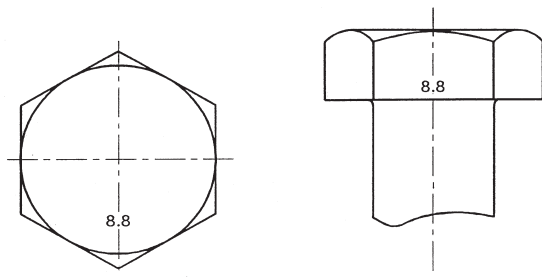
Abb. G: Beispiel für die Kennzeichnung von Sechskantschrauben
